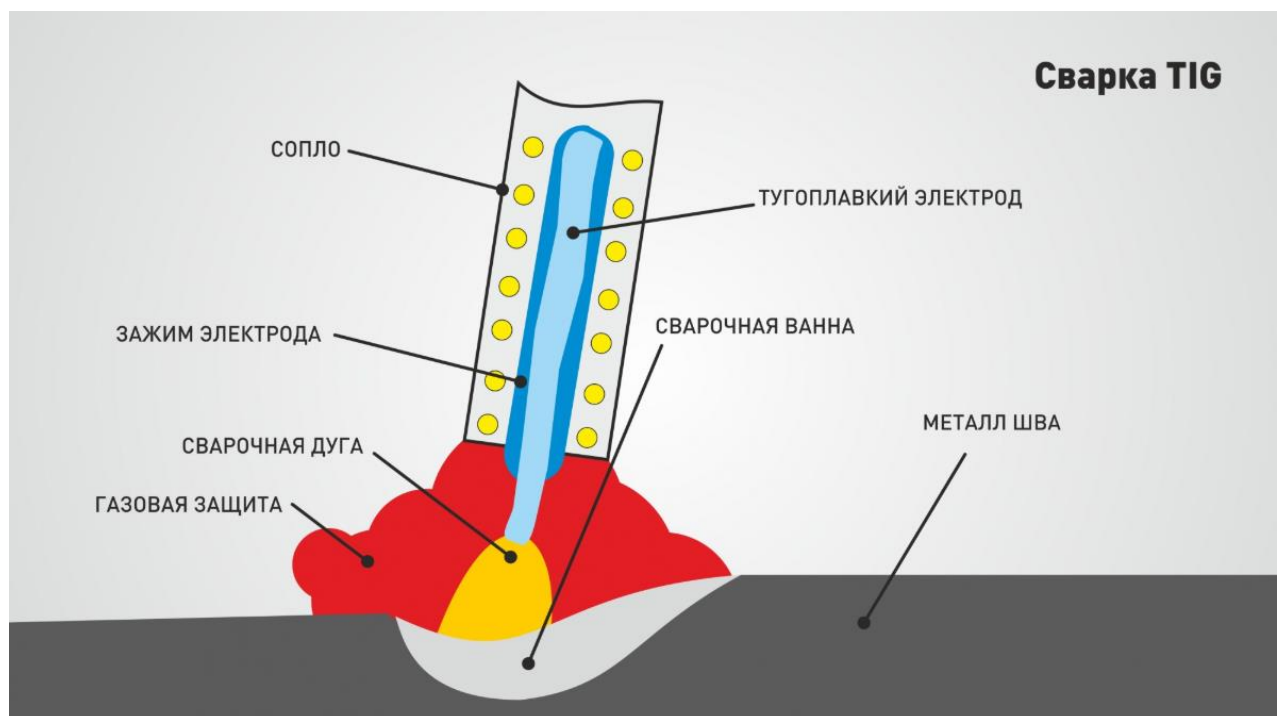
TIG зварювання. Ресурс [39]
